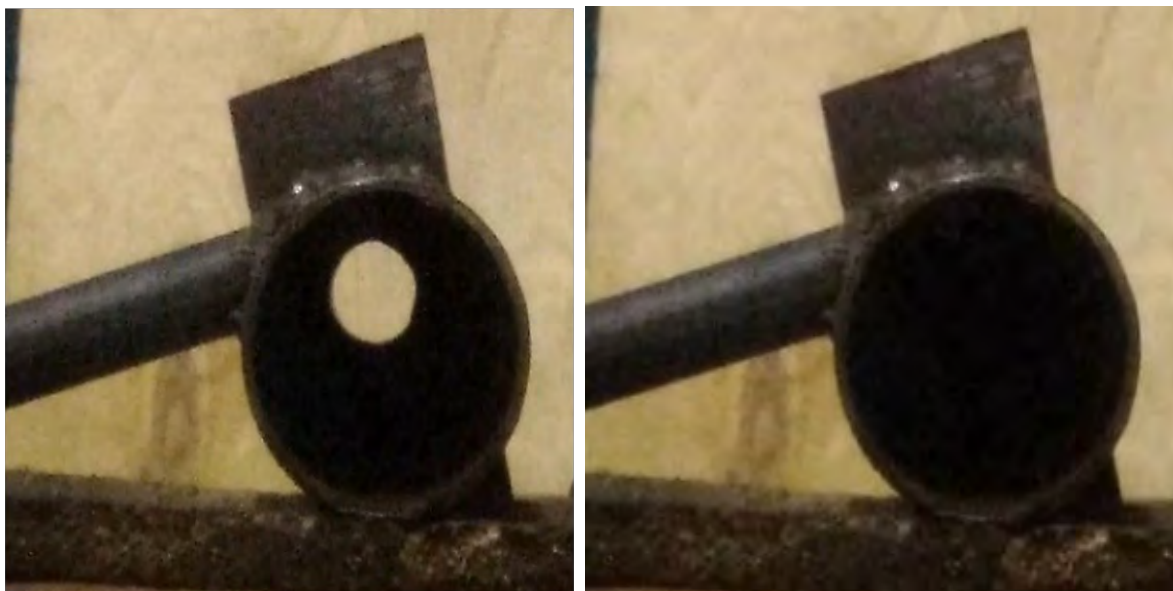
Внешний вид корпусов двух типов вихревых труб - прямоточного и противоточного исполнения без дросселирующего конуса.
